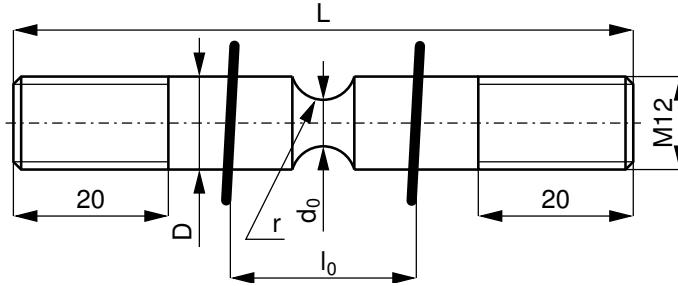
Gekerbte Rundzugproben mit Messmarken für die Dehnungsmessung
